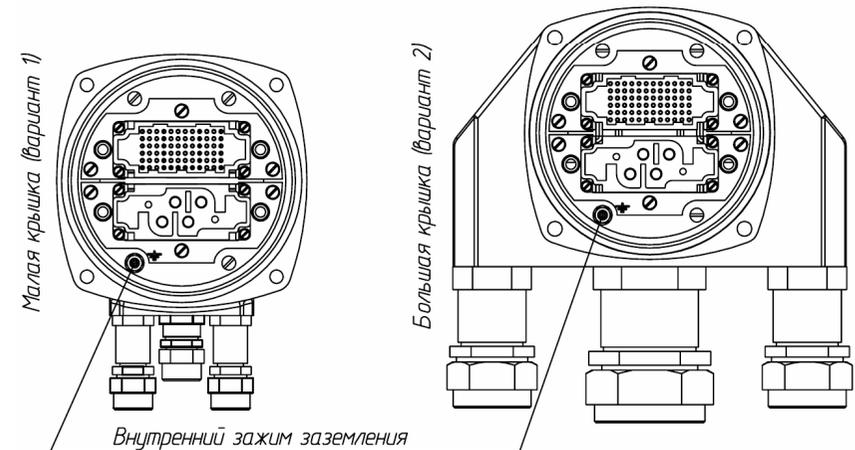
Модуль питания привода с кабельными вводами со снятой крышкой:
